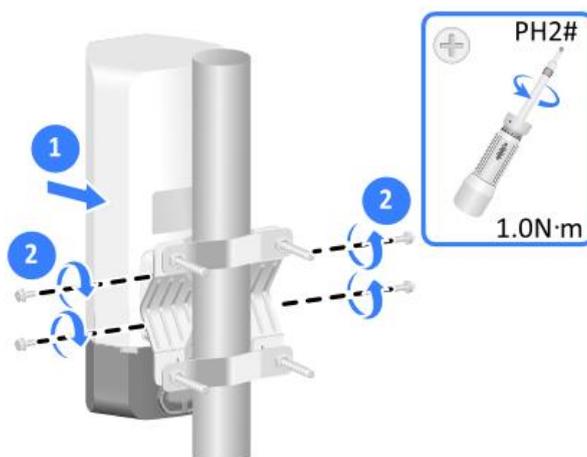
Asegure el Dispositivo al Soporte de Montaje
